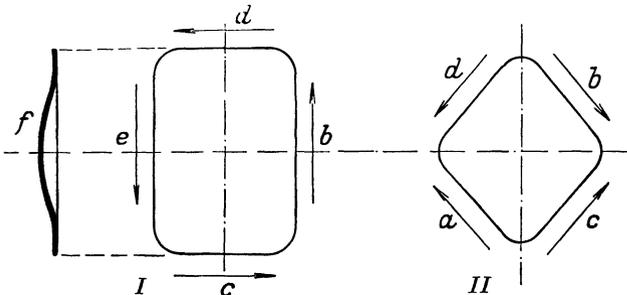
Einschweißen von Flickern bei Dampfkesseln.
